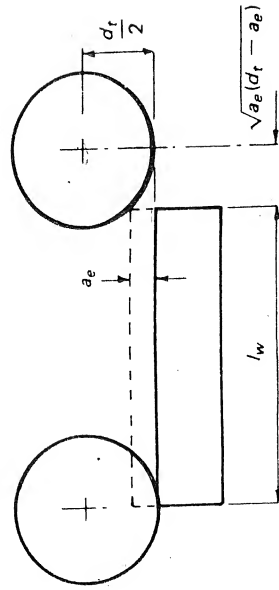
Movimiento relativo entre una fresa cilíndrica y la pieza durante el tiempo de mecanizado.
